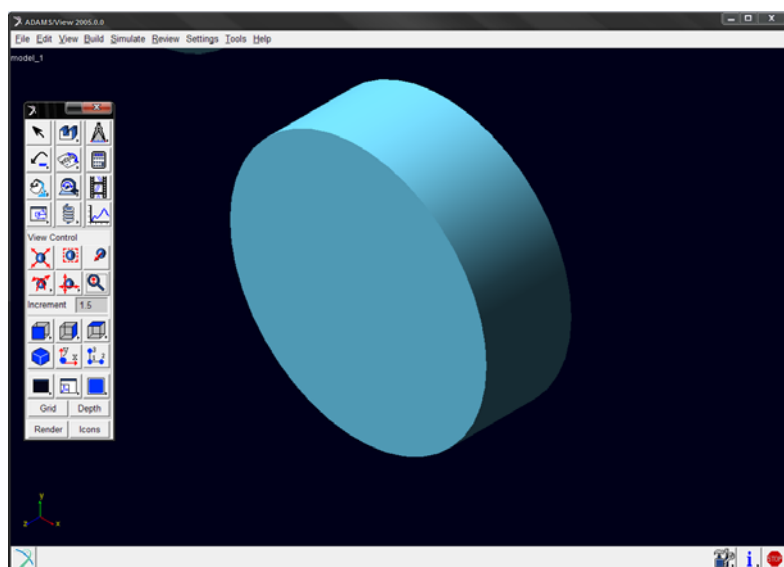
Extrusión del rotor del rodamiento de 9 bolas
